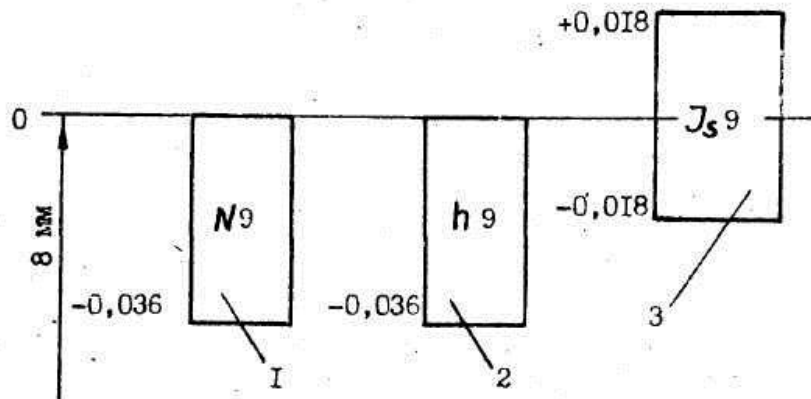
Схема розташування полів допусків нормального шпонкового з'єднання: 1 - поле допуску паза валу, 2 - шпонки, 3 - паза втулки
